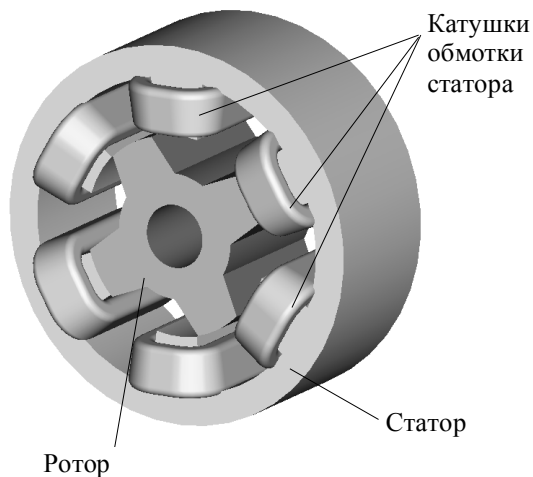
Трехфазный ЭМП ВРД конструкции 6/4
